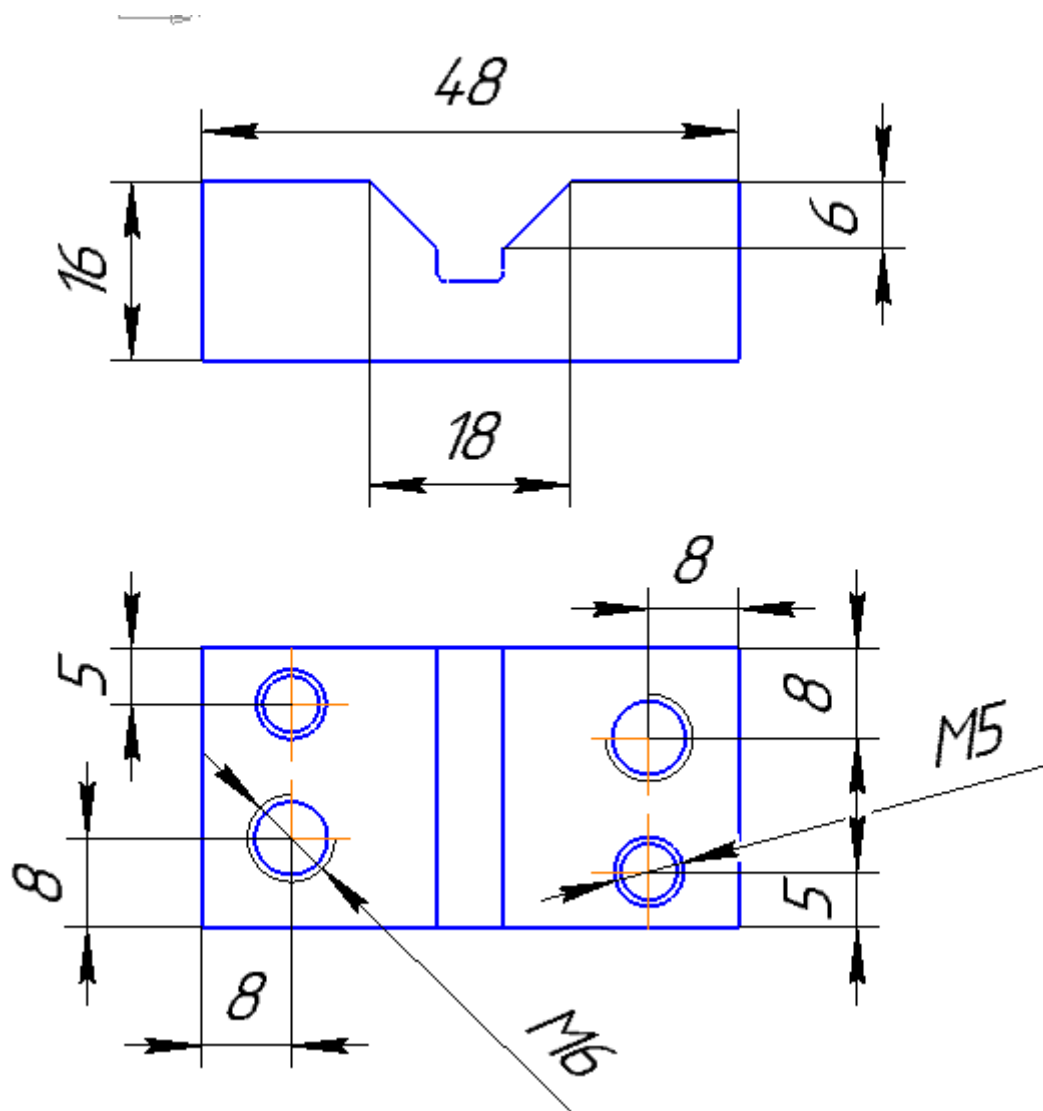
Размеры призмы 7033-0033 ГОСТ 12195-66
